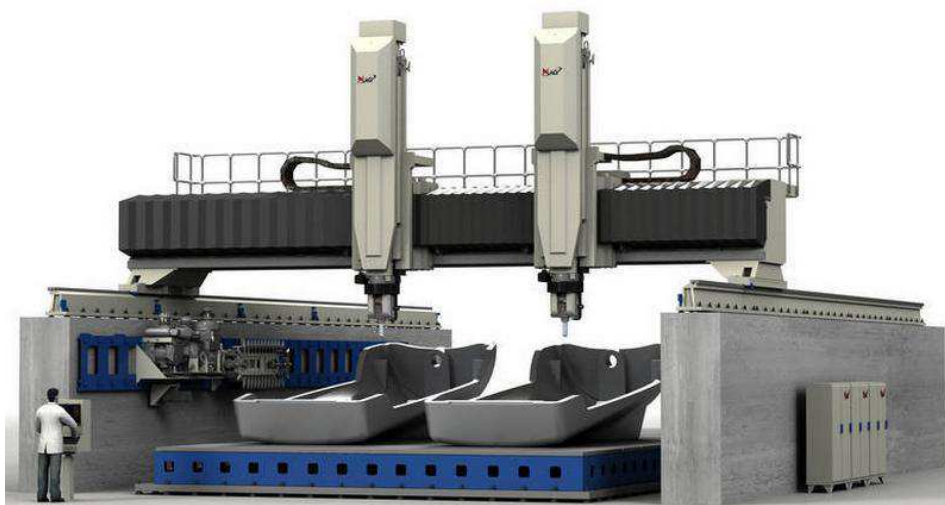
Portálová frézka s posuvným stolem PMB 200140 od firmy PROFIMACH [13]
